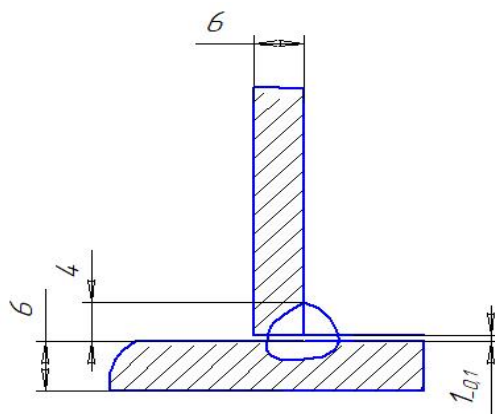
Схема сварного соединения по ГОСТ T1 14771-79
